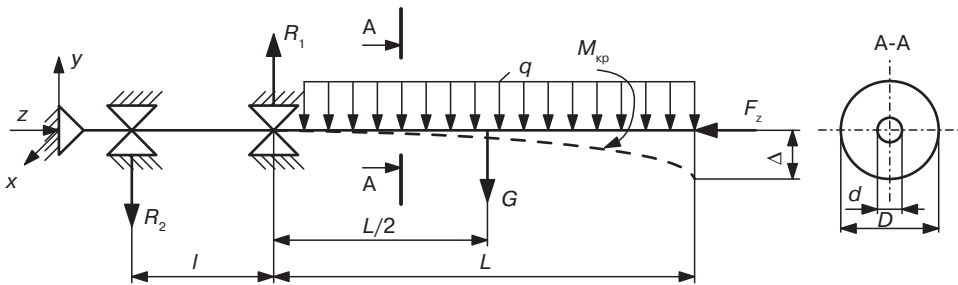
Расчетная схема нагружения шнека и его опор
